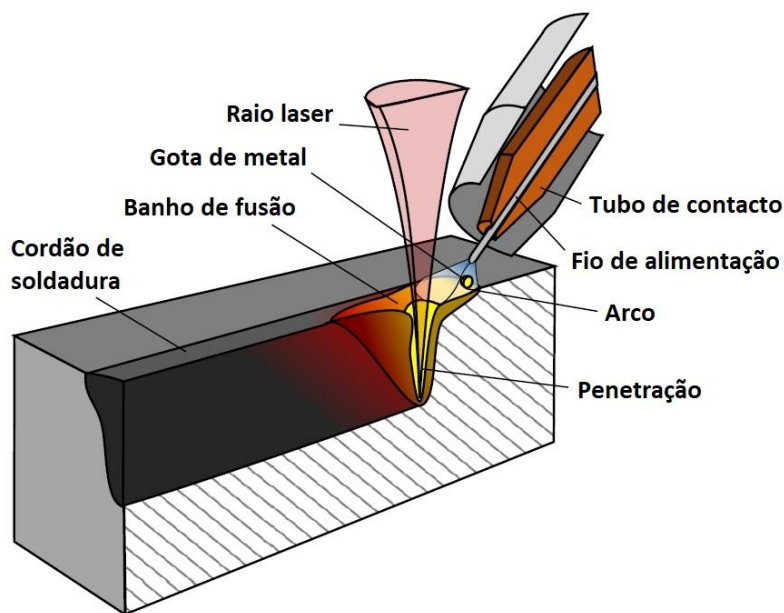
Soldadura Laser com adição de material [Adaptado de (IONIX, HYBRID LASER WELDING, s.d.)].
